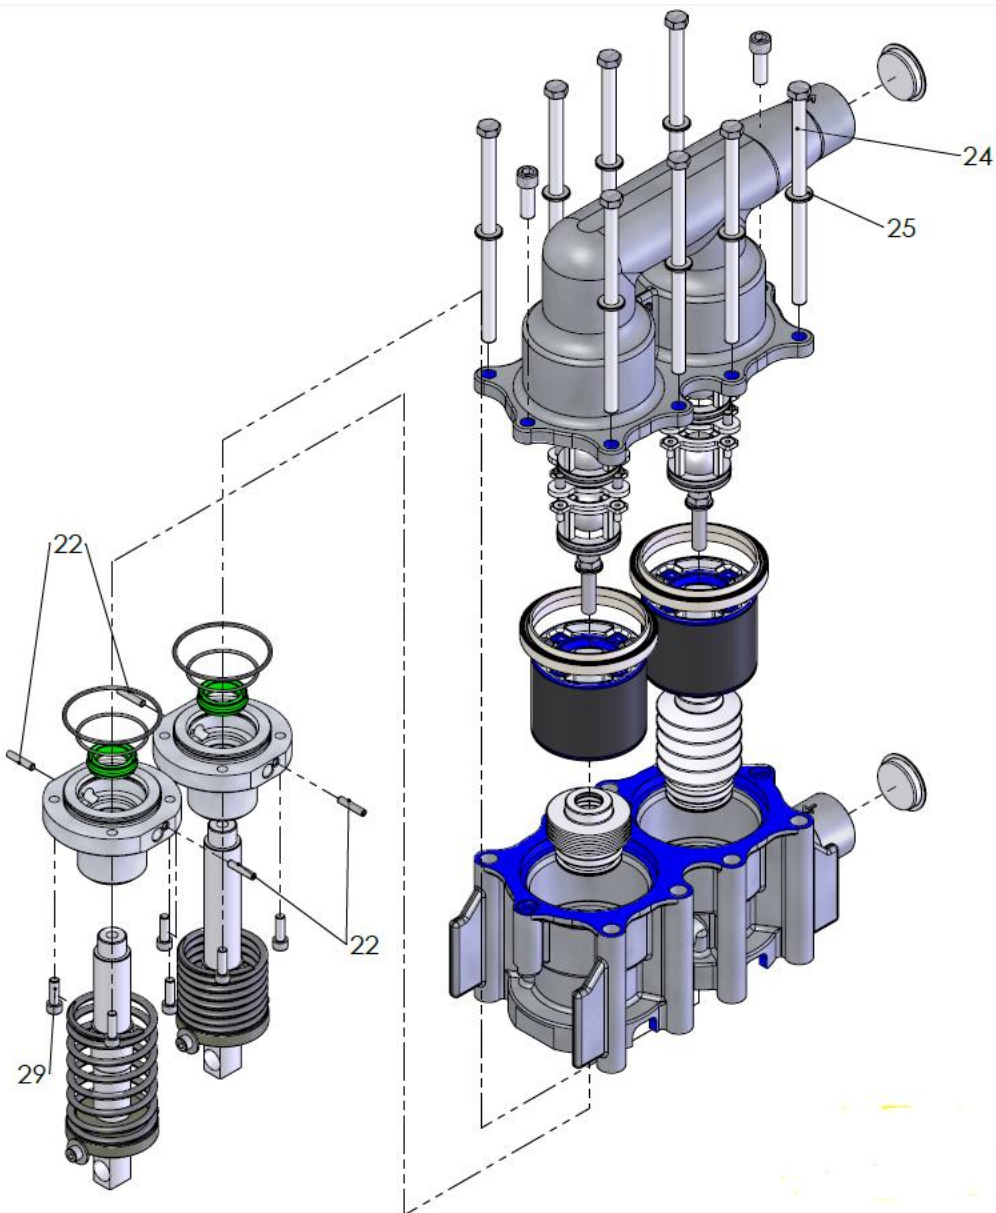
Explosionszeichnung Pumpeneinheit
